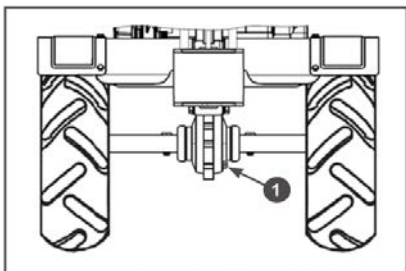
Расположение пробки для слива масла из картера коробки передач (вид сзади)
